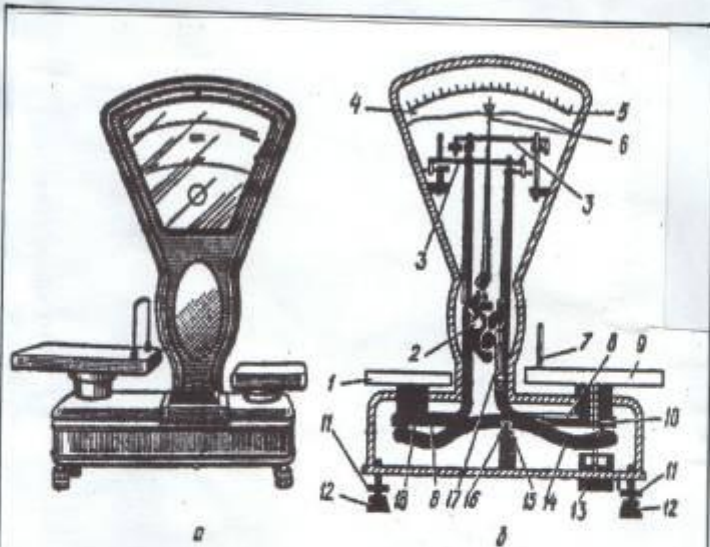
Настольные циферблатные весы РН-10Ц13 (а — общий вид, б — схема устройства): 1 — гириная платформа; 2 — квадрант; 3 — планки; 4 — циферблат; 5 — шкала циферблата; 6 — стрелка циферблата; 7 — барьер платформы; 8 — штанги; 9 — грузоприемная платформа; 10 — подушки; 11 — контргайки; 12 — винтовые ножки; 13 — масляный тормоз; 14 — коромысло; 15 — подушка опорной призмы; 16 — опорная призма; 17 — тяга квадранта; 18 — тарировочная камера
